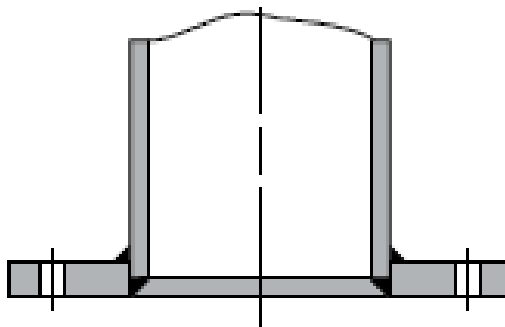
Esquema junta brida y tubería soldada
